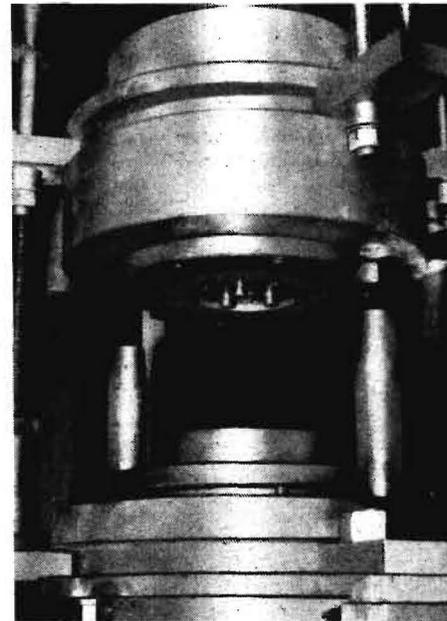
Umformtechnische Verfahrenslösung zur Aufarbeitung von Kolbenbolzen
